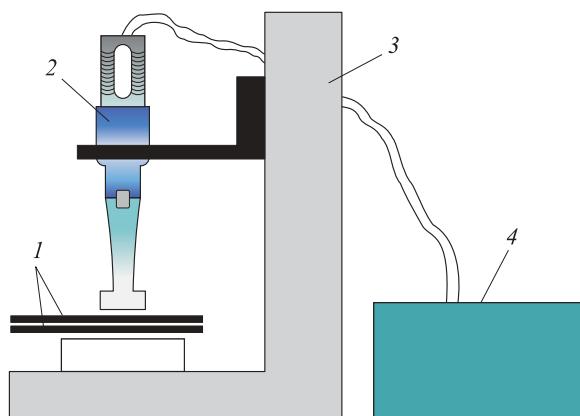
Схема установки для ультразвуковой сварки проводников: 1 — свариваемые проводники; 2 — ультразвуковой преобразователь; 3 — механический пресс; 4 — ультразвуковой генератор
